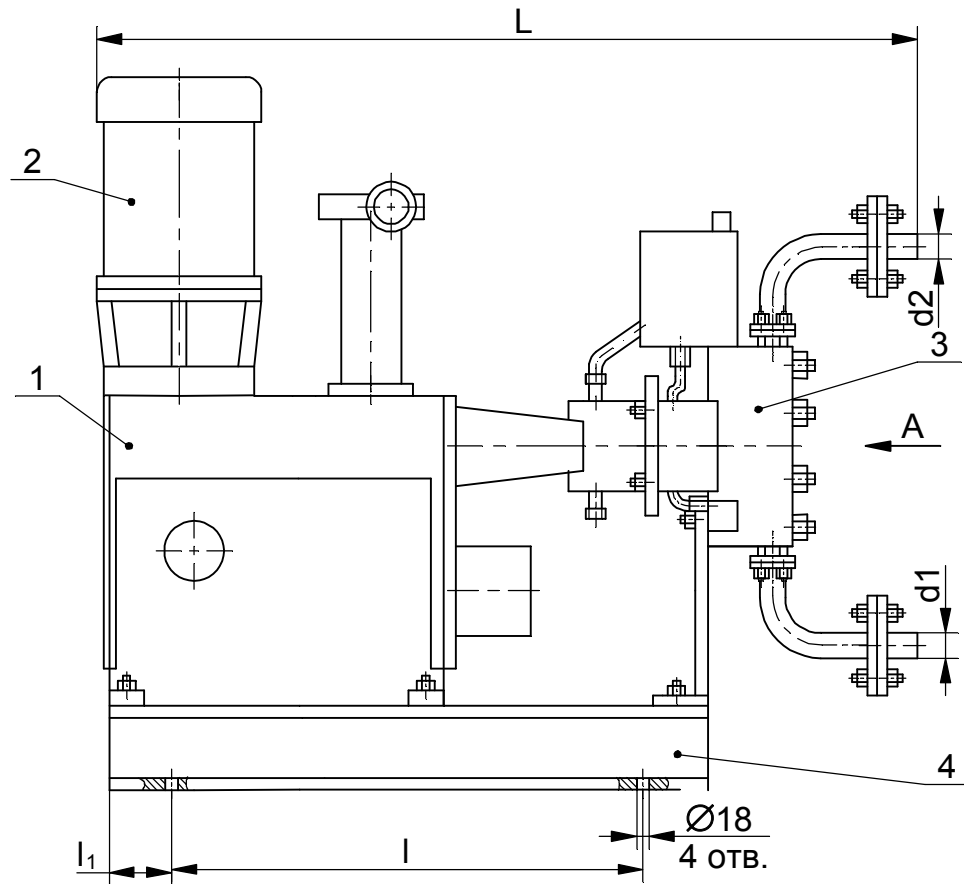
Внешний вид агрегата с параметрами номинального режима 500/100; 800/63
